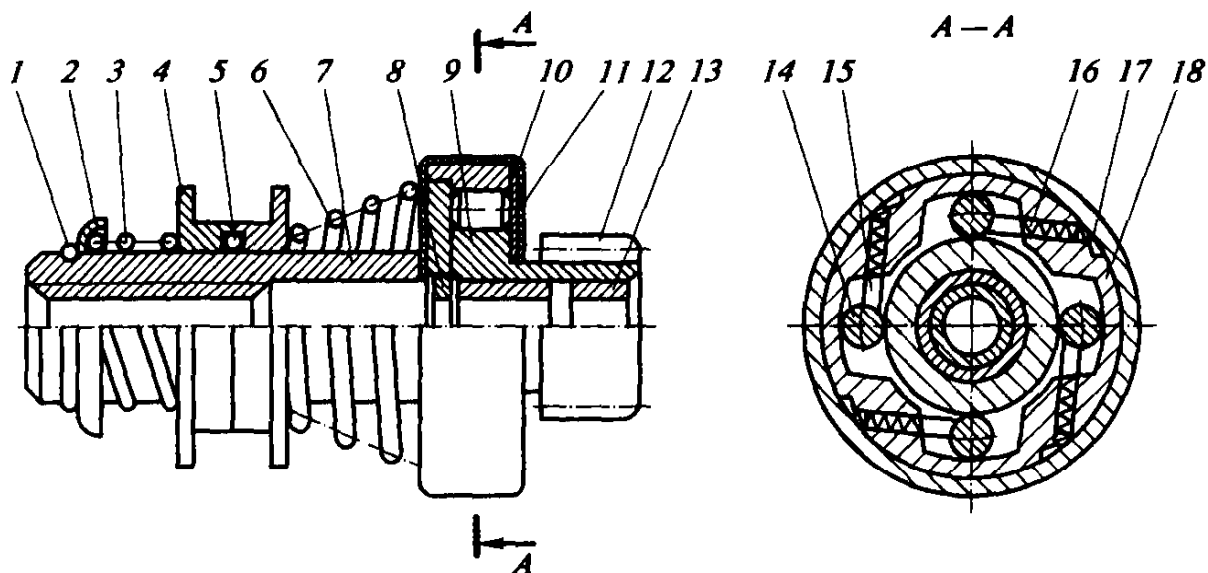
Приводной механизм стартера с роликовой муфтой свободного хода:
